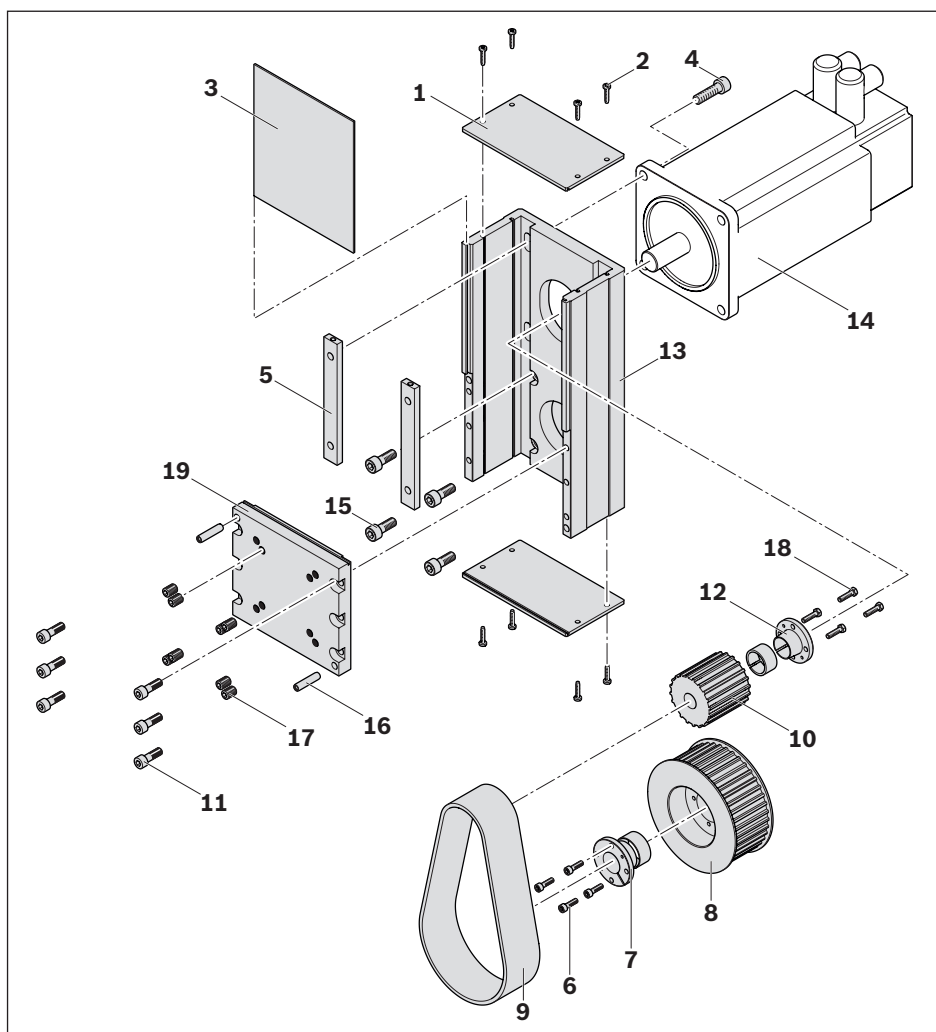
Desmontaje del motor y de la transmisión por correa dentada sin contra-apoyo
